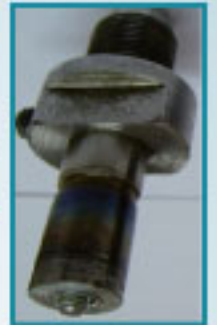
Photo réelle de l'outil de soudage FSW réalisé.
